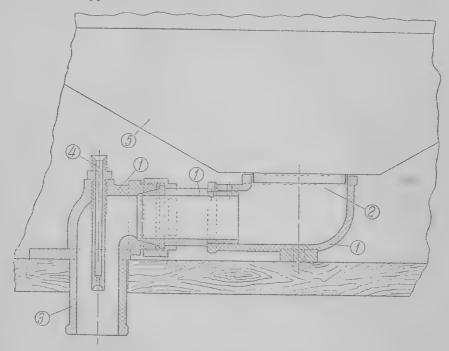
Воздушная песочинца Плащинского: 1 — корпус, 2 — отверстие, 3 — патрубок, 4 — сопло, 5 — песочный ящик.
